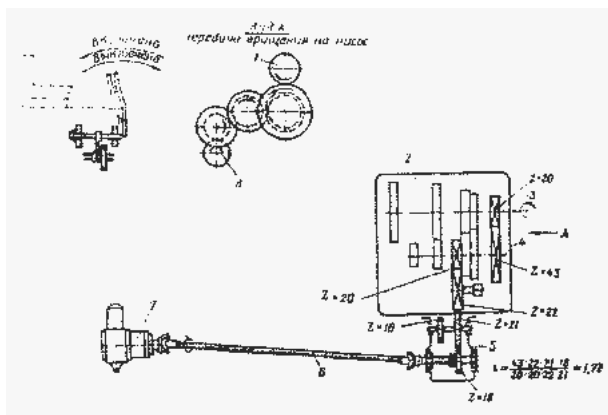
Схема привода насоса СВН-80А от коробки передач ЗиЛ-131 АРС-14ПМ
